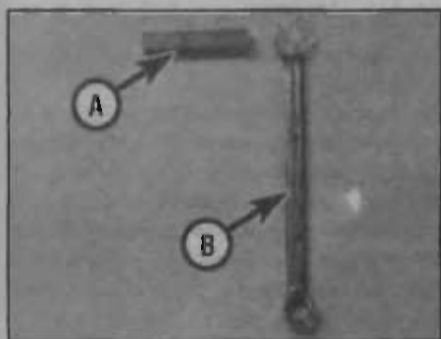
Квадратный стержень (А) и гаечный ключ (В), используемые для поворота шкива механизма натяжения зубчатого ремня
